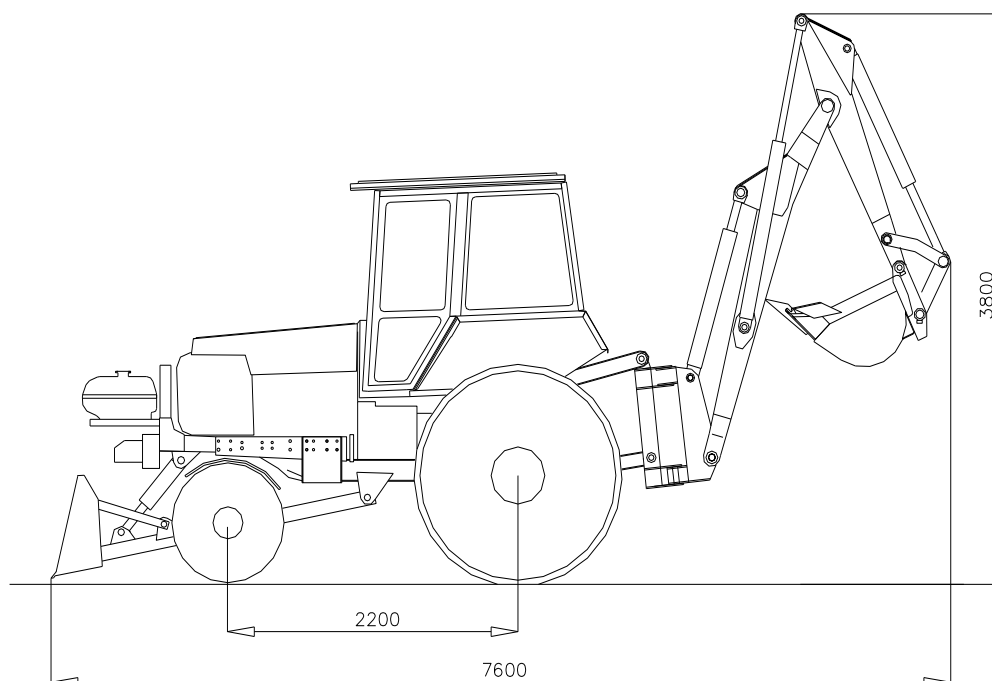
Общий вид землеройно-экскаваторных оборудований многоцелевой машины на базе трактора ТТЗ-80.10
